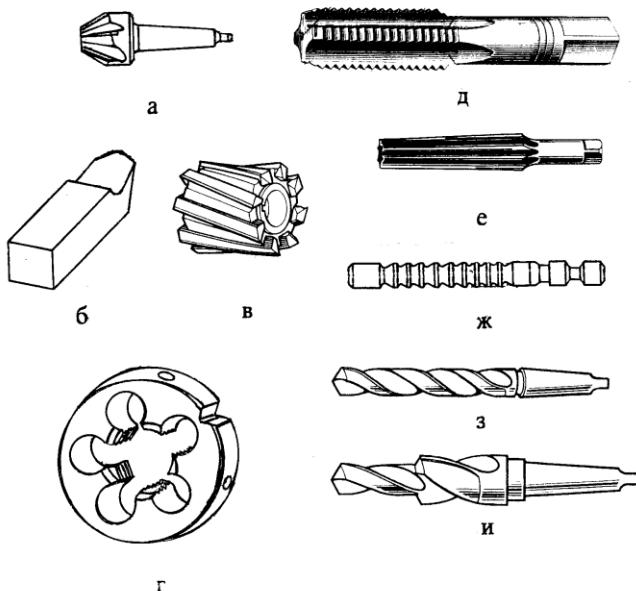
Лезвийный режущий инструмент: *а* – конический зенкер; *б* – прямой проходной резец; *в* – цилиндрическая фреза; *г* – круглая плашка; *д* – метчик; *е* – коническая чистовая развертка; *ж* – круглая протяжка; *з* – спиральное сверло с коническим хвостовиком; *и* – комбинированное сверло-зенкер
